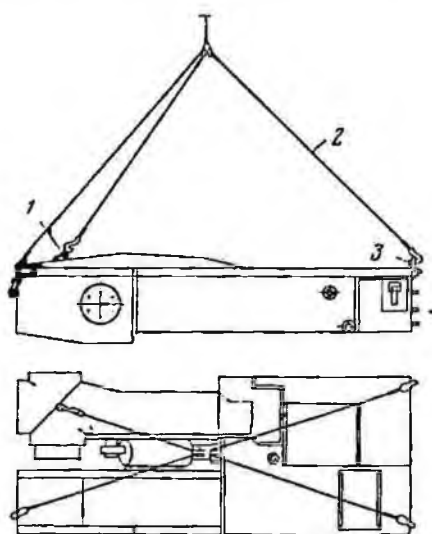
Строповка центрального редуктора очистного комбайна 1ГШ68:
